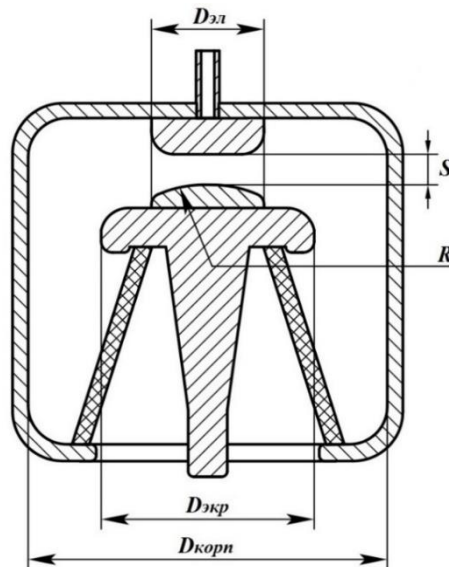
Базовая конструкция разрядника-обострителя:
